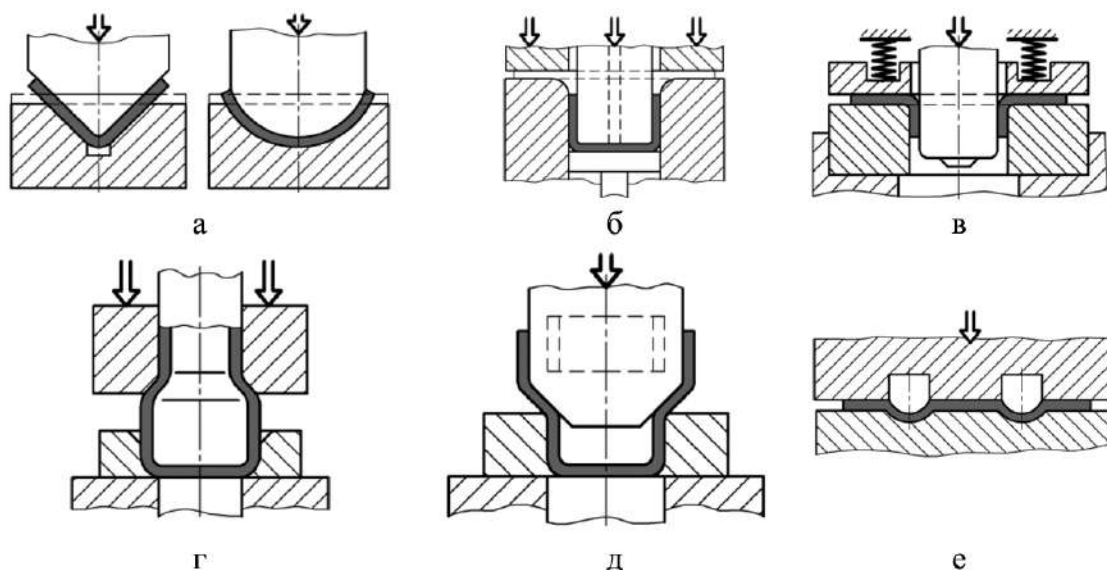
Формоутворювальні операції листового штампування [12]:
